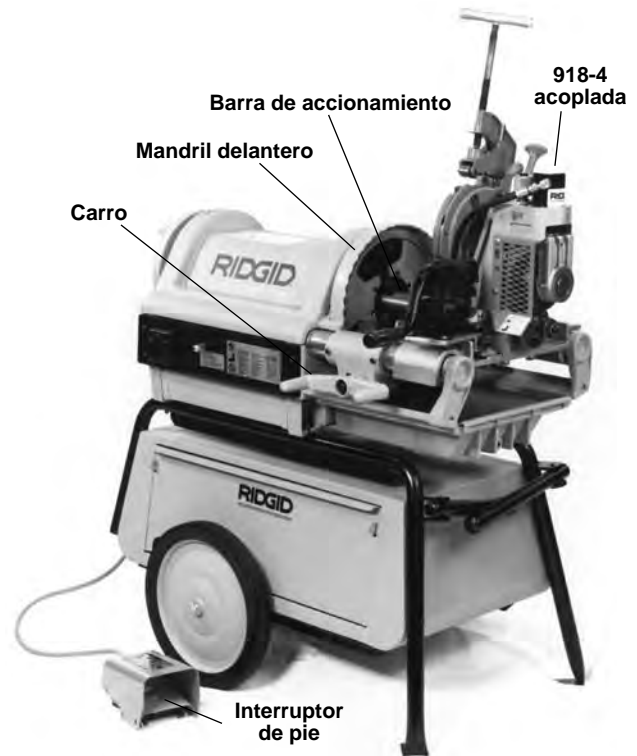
Ranuradora a rodillos No. 918-4 montada a la Máquina Roscadora 1224
